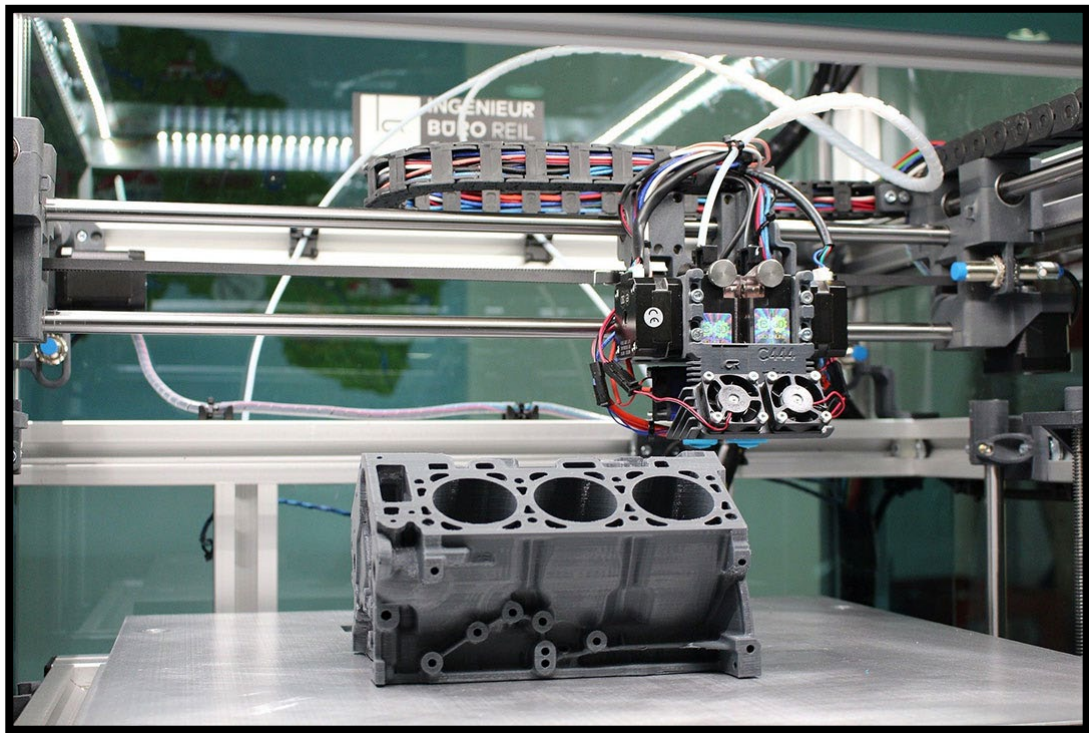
Impresión en 3D de un motor de combustión interna [38]
